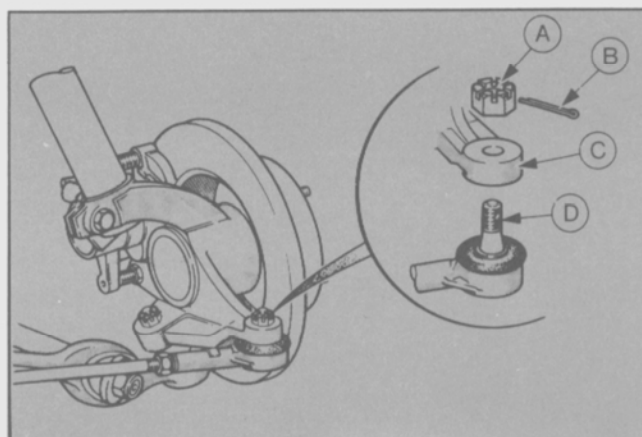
Montaje del extremo de la barra de acoplamiento.
